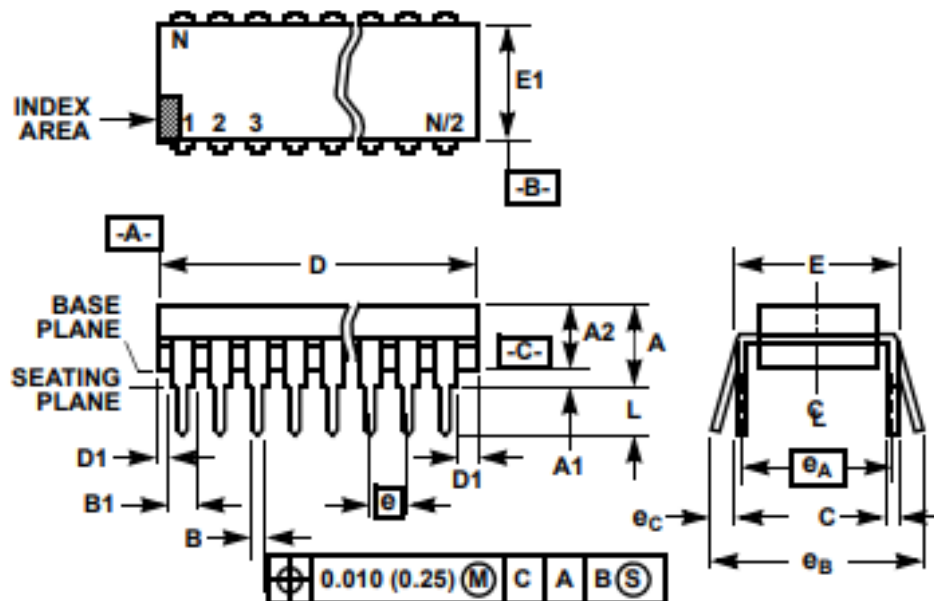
Габаритный чертеж драйвера типа ISL83202IBZT
